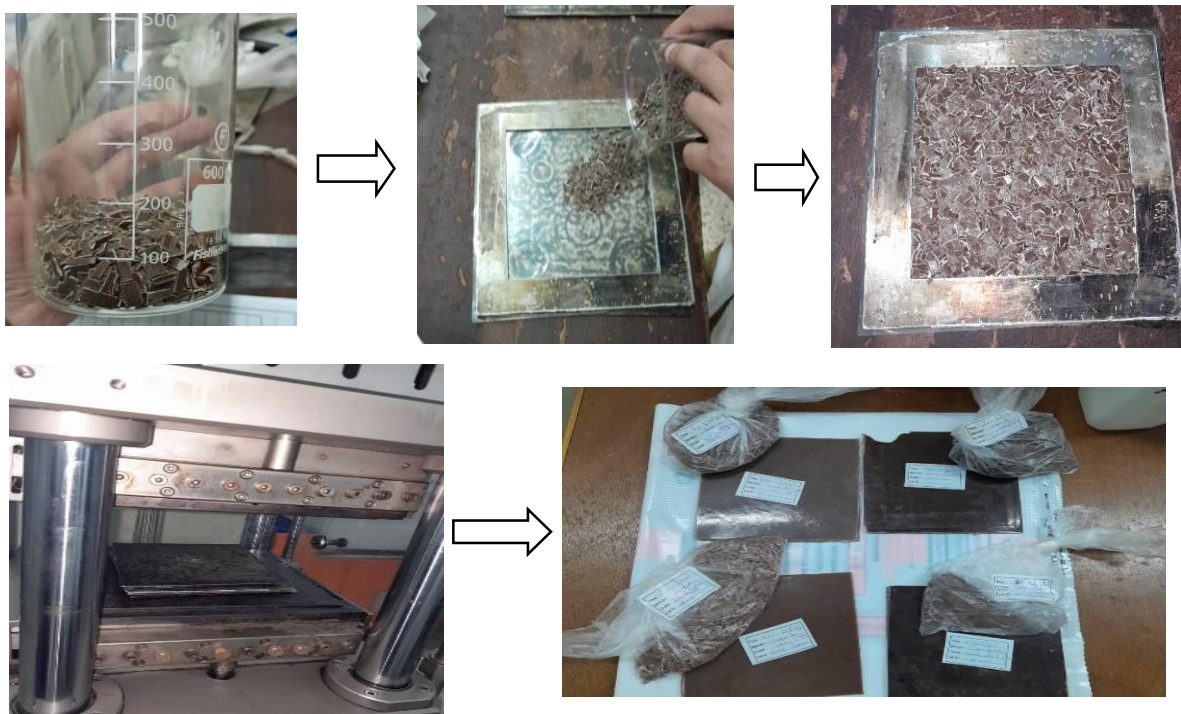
Opération de la méthode de thermocompression par la presse hydraulique.
